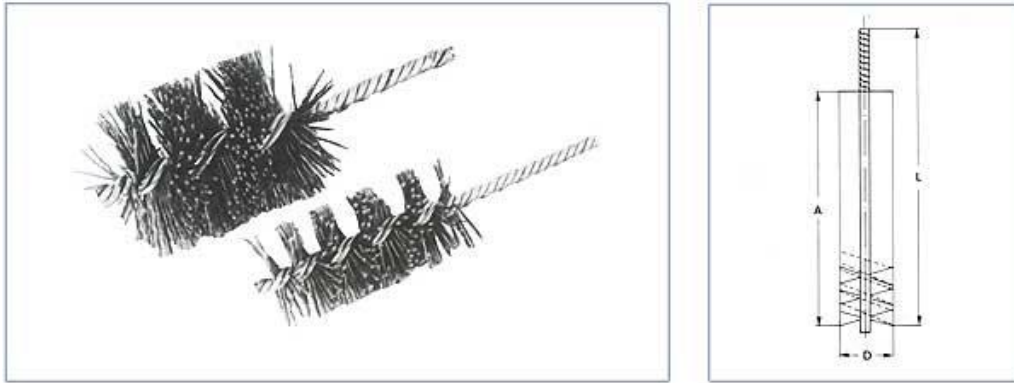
Полимерно-абразивные щетки для обработки отверстий
